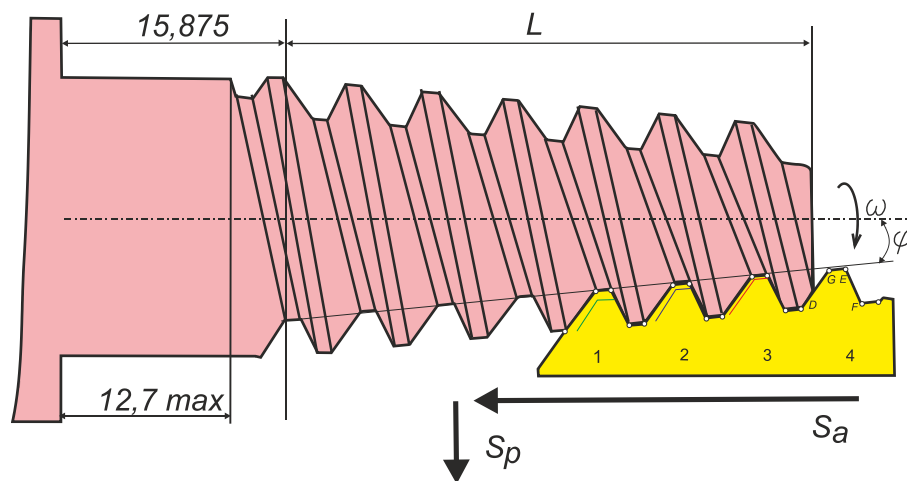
Схема початку фінішного проходу 4-ниткової гребінки під-час виконання замкової нарізі . S_a – повздовжня подача гребінки, S_p -поперечна подача гребінки, ω - рух обертання заготовки навколо осі.
